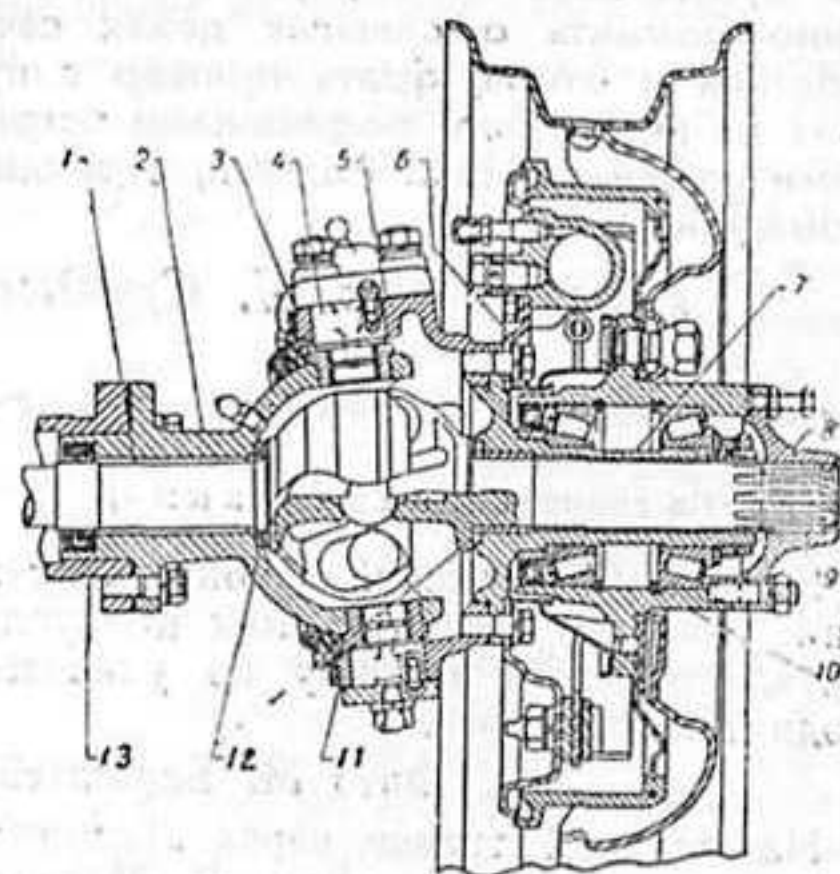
Поворотный кулак переднего ведущего моста. 1 — ведущий кулак, 2 — шаровая опора, 3 и 11 — регулировочные прокладки, 4 — шкворень, 5 — корпус поворотного кулака, 6 — болт крепления цапфы поворотного кулака к корпусу, 7 — цапфа поворотного кулака, 8 — фланец ступицы, 9 — ведомый кулак, 10 — ступица, 12 — упорные шайбы шарнира равных угловых скоростей, 13 — кожух полуоси.
